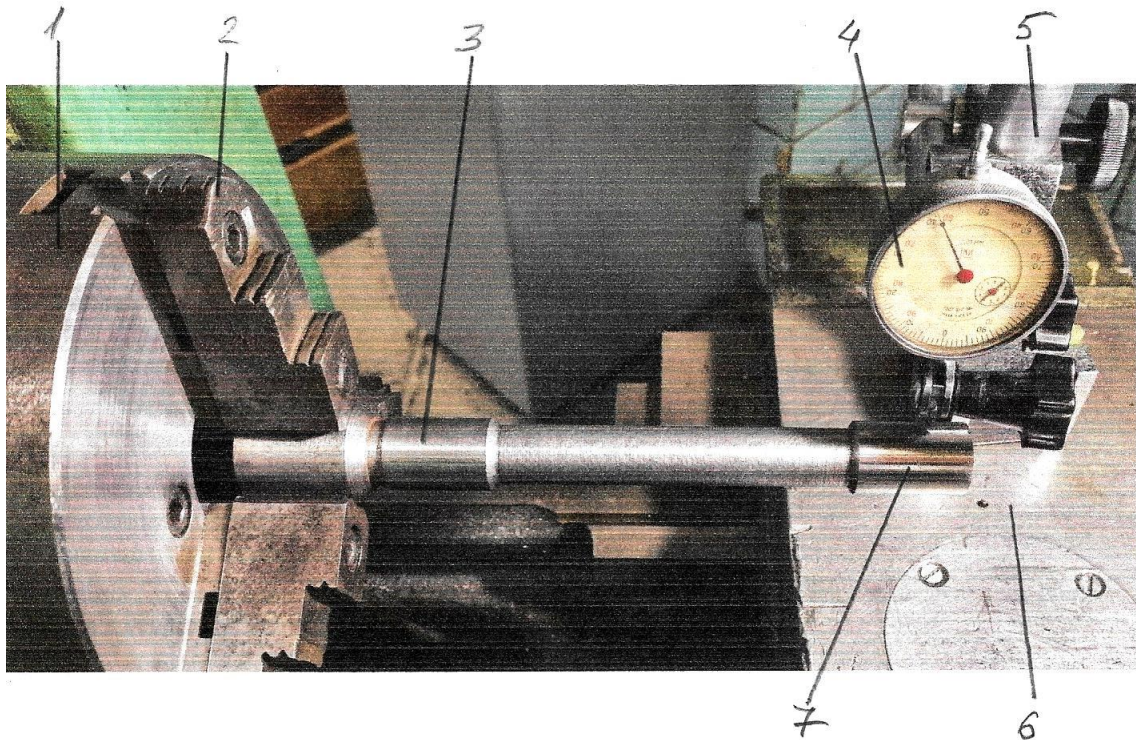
Измерение биения заготовки при закреплении в трехкулачковом патроне: 1 - корпус патрона; 2 – кулачок; 3 – шейка В контрольной оправки; 4 – индикатор; 5 – магнитная стойка; 6 – суппорт токарного станка; 7 – шейка С контрольной оправки
